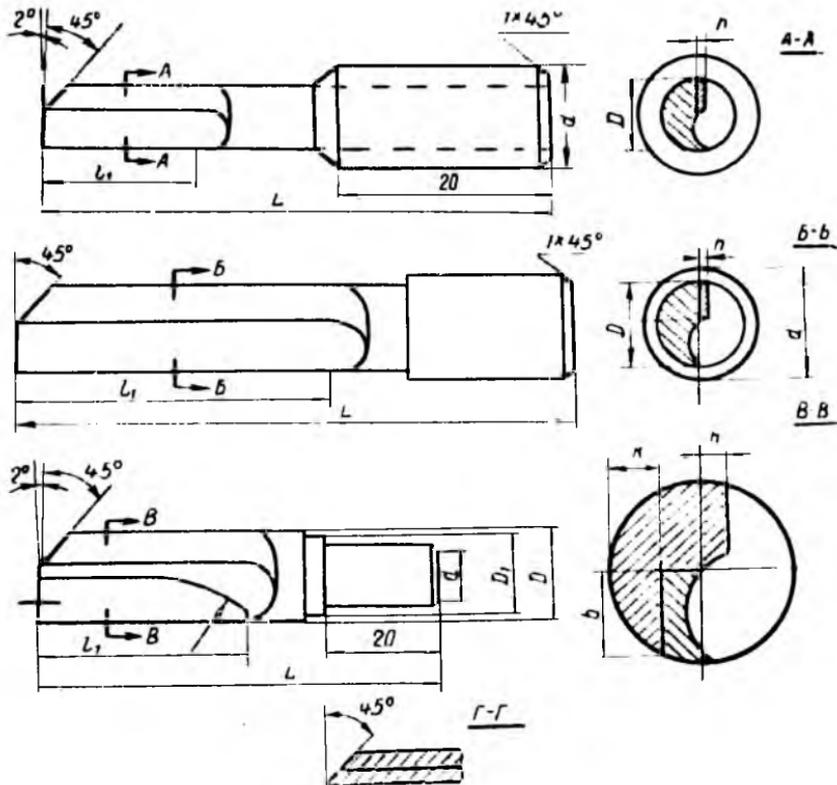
Фрезы концевые цилиндрические незатылованные односторонние с твердым сплавом
